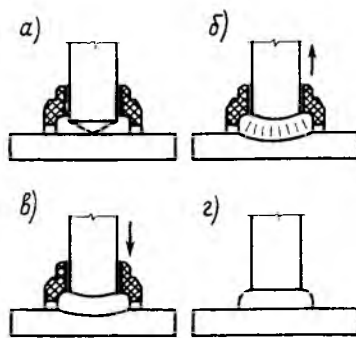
Стадии дугоконтактной сварки стержней в керамических кольцах
